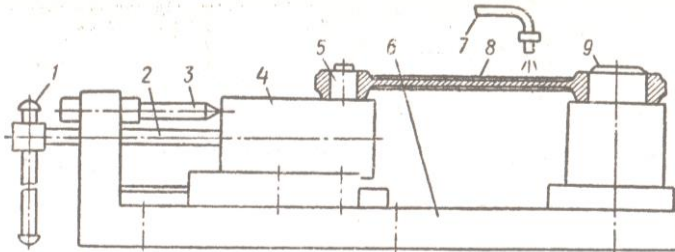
Схема пристрою для розтягування шатунів: 1 – рукоятка; 2 – ходовий гвинт; 3 – обмежувач ходу; 4 – повзун; 5 – рухома опора; 6 – основа; 7 – газовий пальник; 8 – шатун; 9 – нерухома опора
